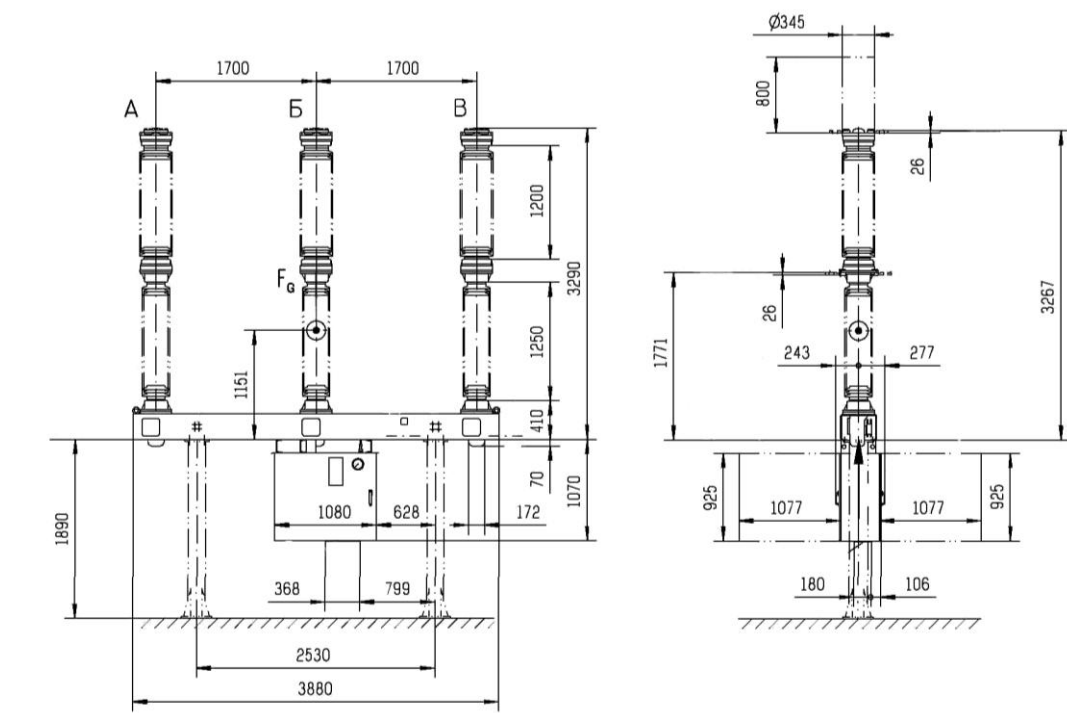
Внешний вид и габаритные размеры выключателя ЗАР1FG-145-С
